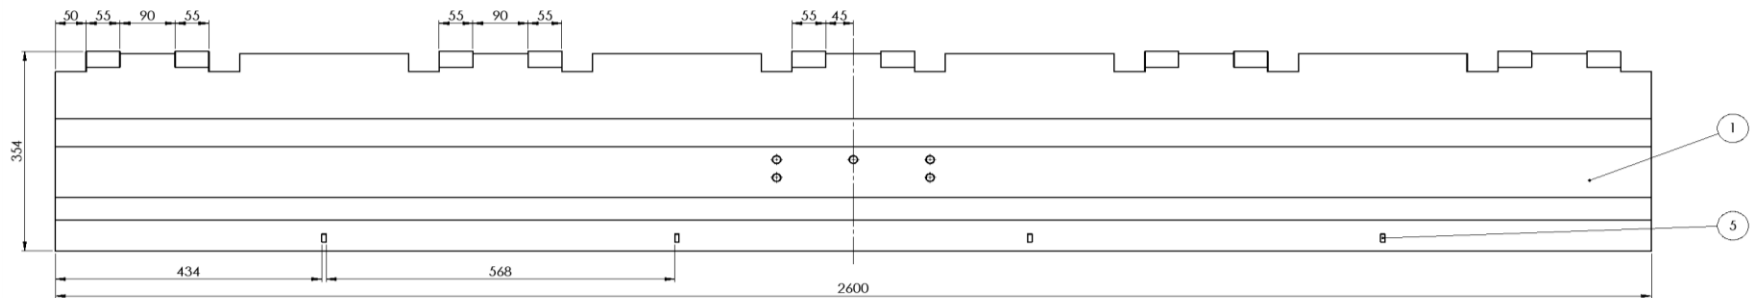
Vista superior del ensamble de la rampa. Fuente: Elaboración propia.
